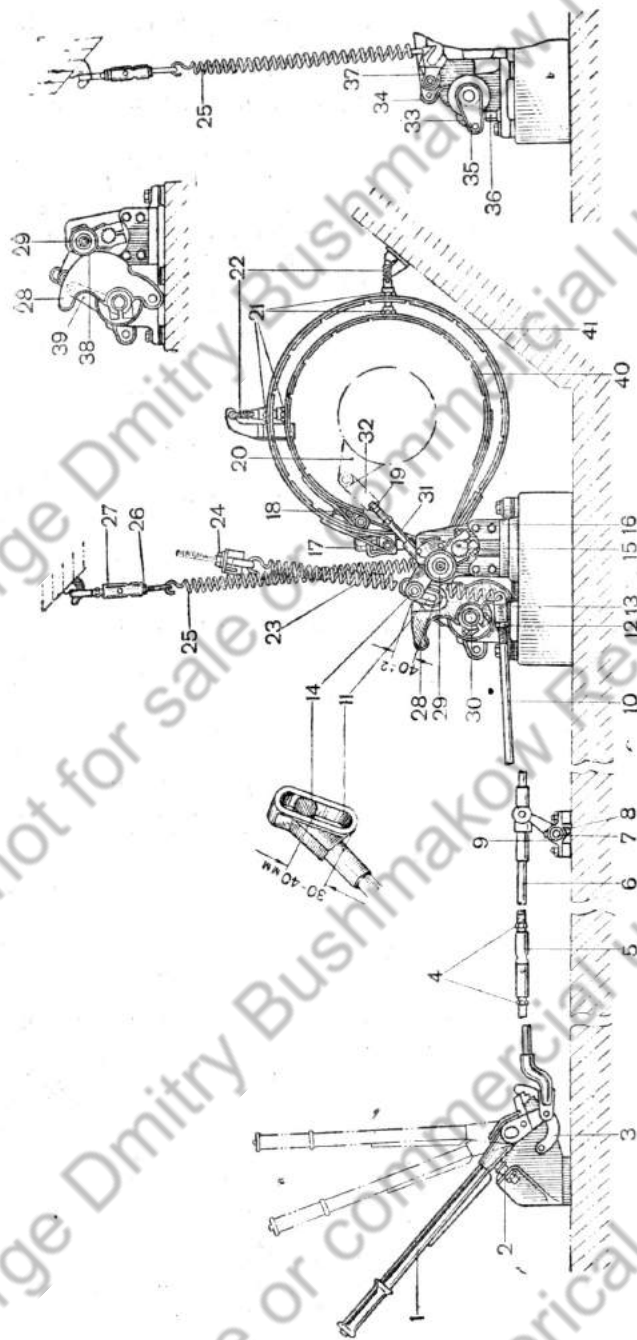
Привод управления планетарным механизмом поворота (плоскостной чертёж).
